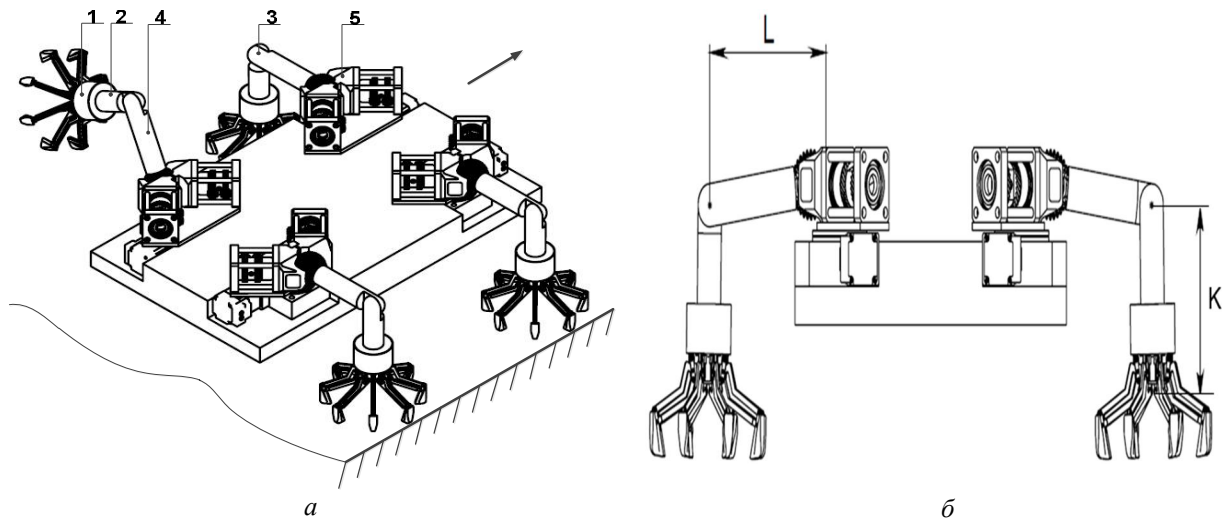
НРК з БМ: а – вид зверху; б – вид спереду
